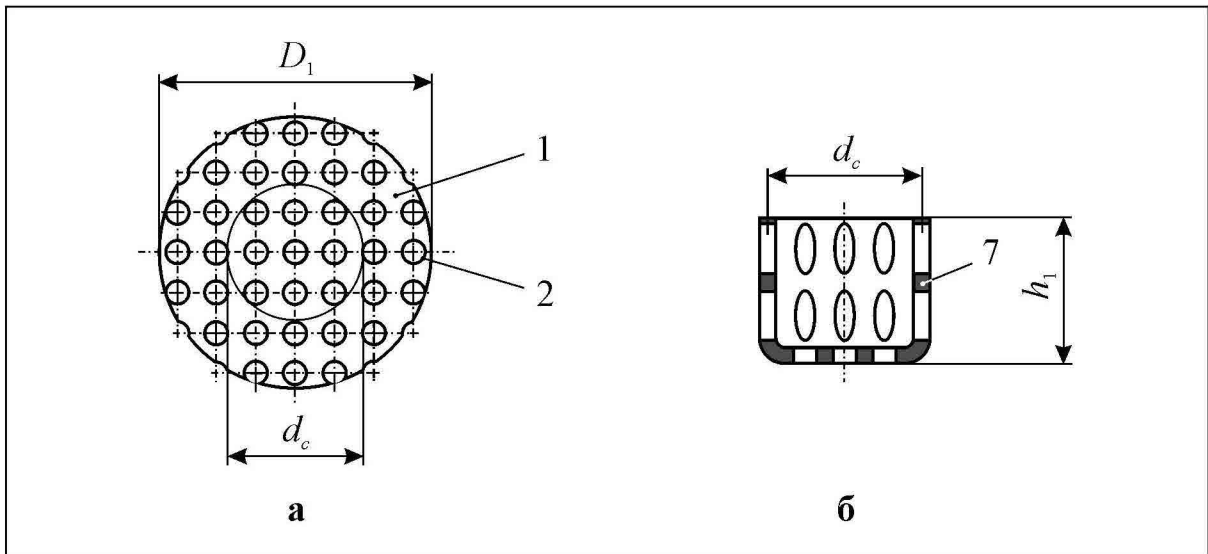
Заготовка (а) та деталь (б) після витягування за пунктом 1
